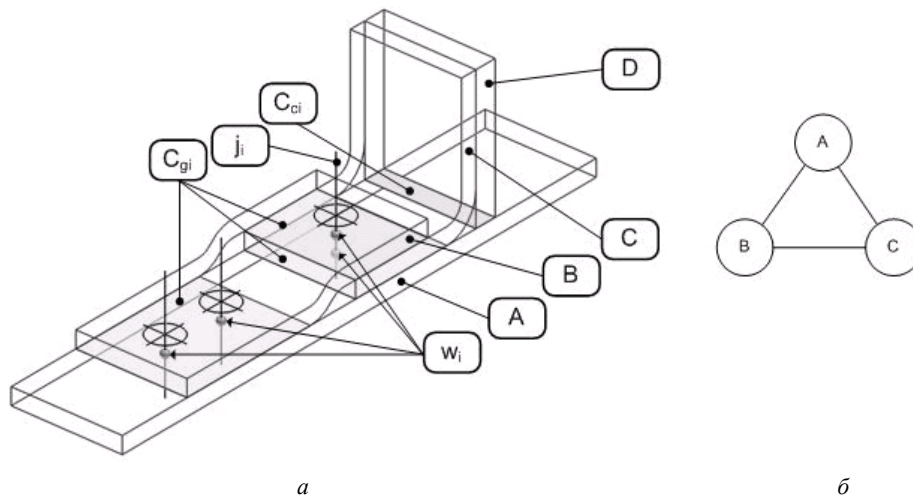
Собираемый пакет: а – сборочный узел; б – граф сопряжений сборочного узла
